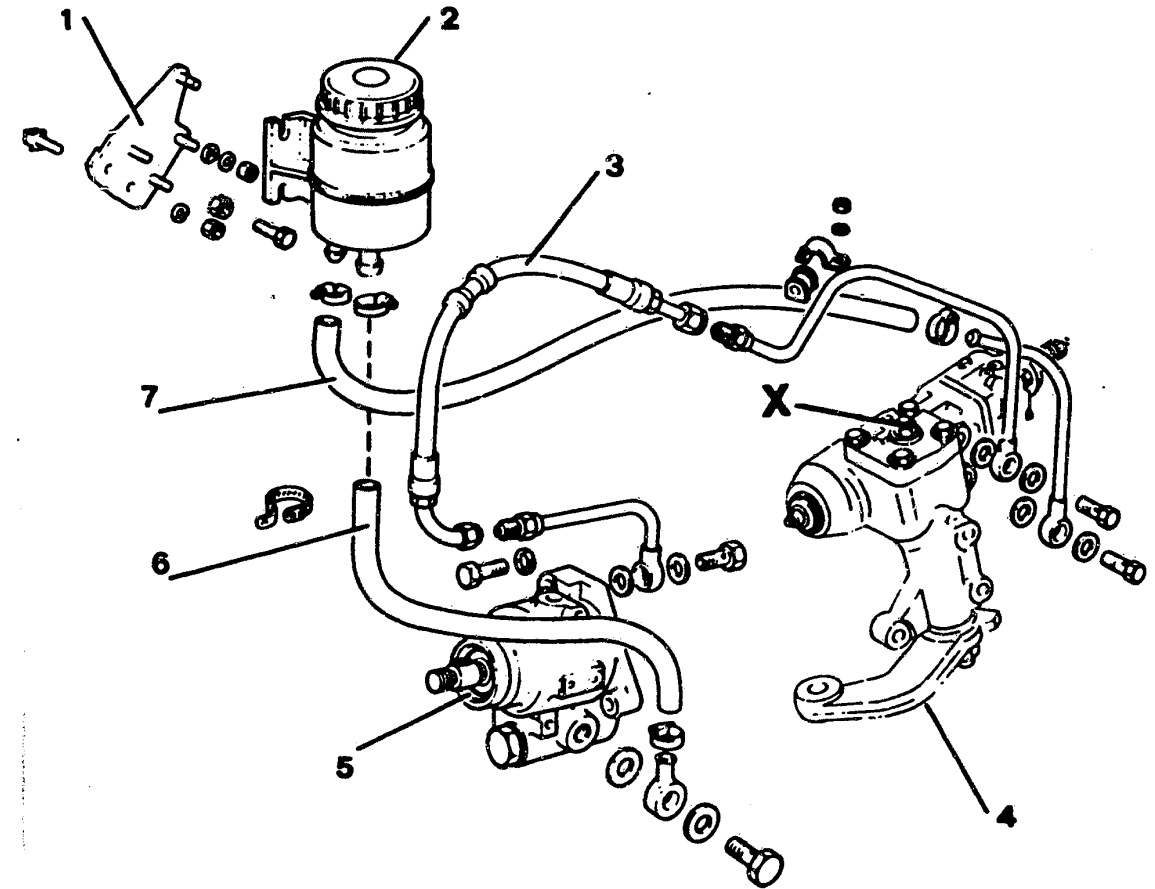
Einzelteile der hydraulisch unterstützten Kugelumlauflenkung. 1 Befestigungsplatte – 2 Behälter – 3 Öldruckleitung – 4 Lenkhebel – 5 Hydraulikpumpe – 6 Ölzufluss – 7 Ölrückflussleitung. Schraube «X» dient der Einstellung des Lenkungsspiels.
